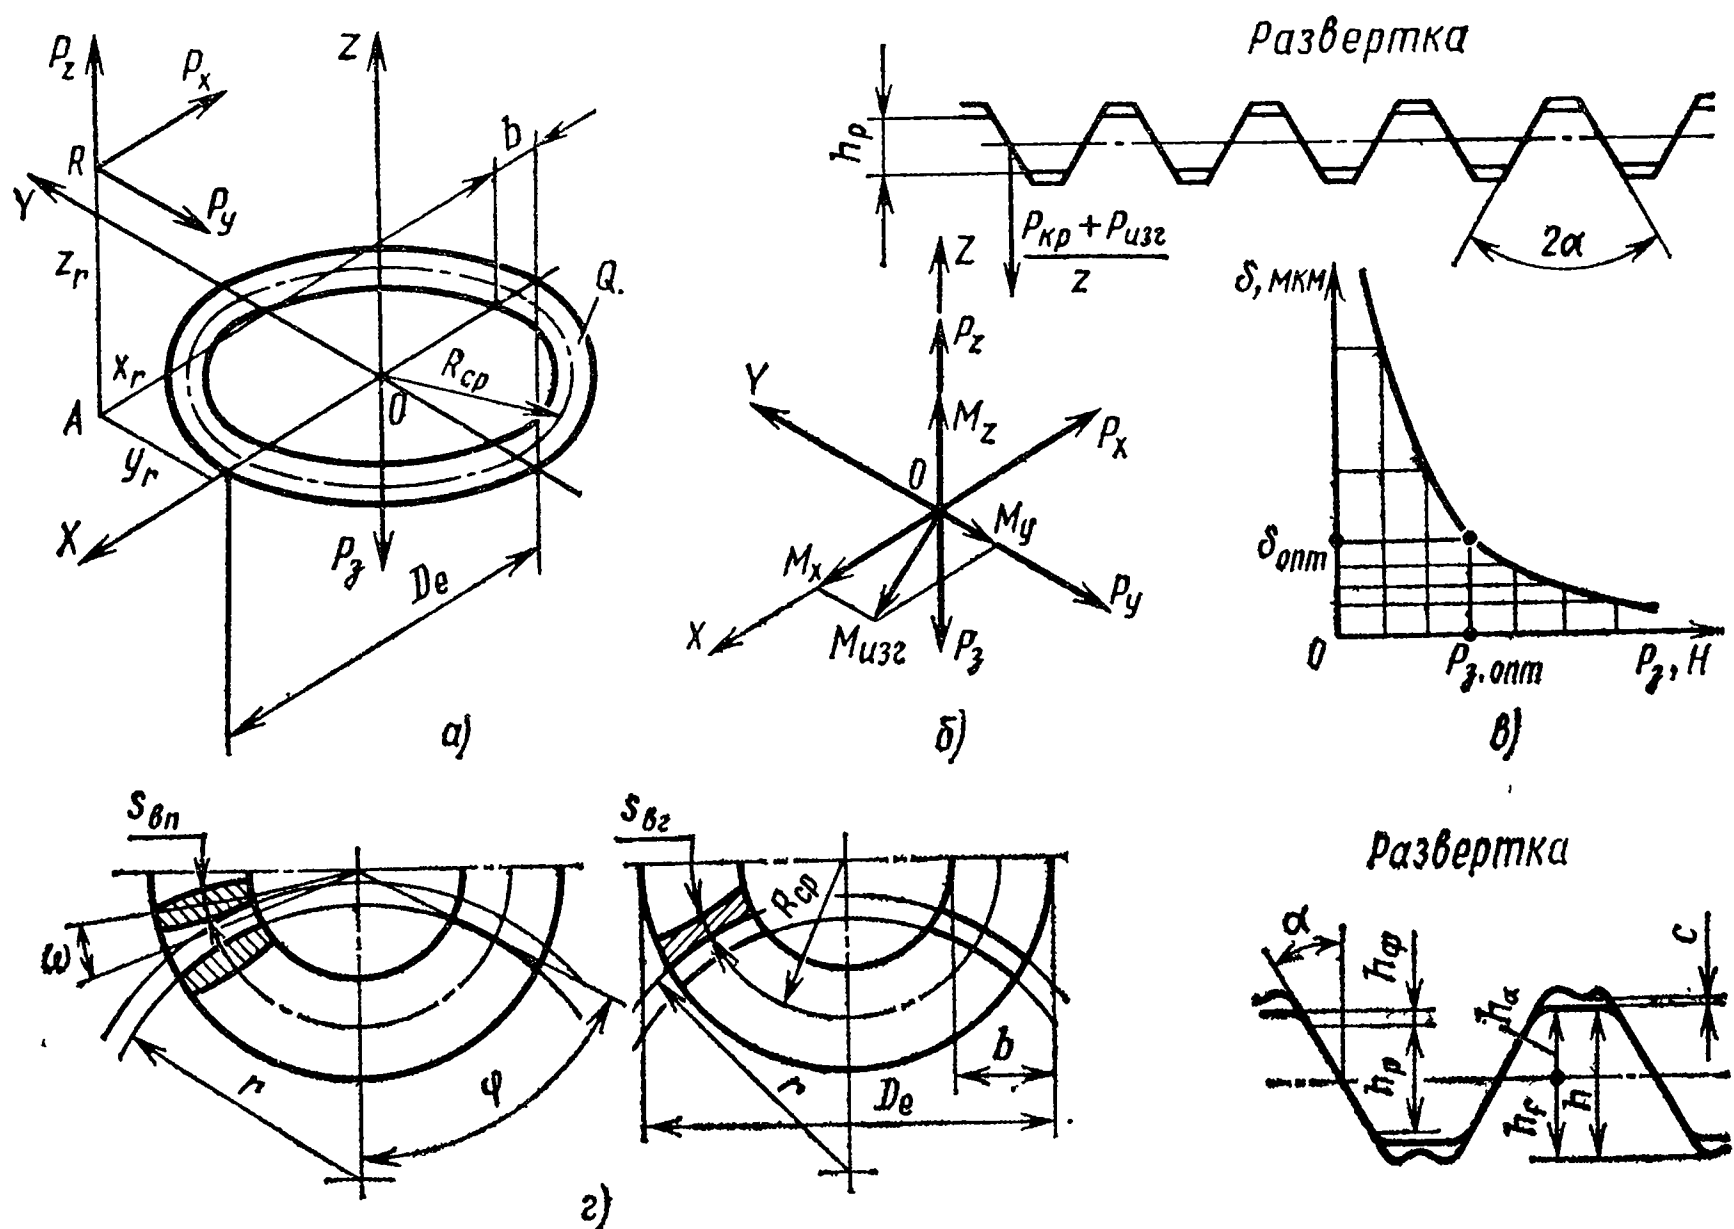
Схема нагружения и параметры зубчатых муфт:
